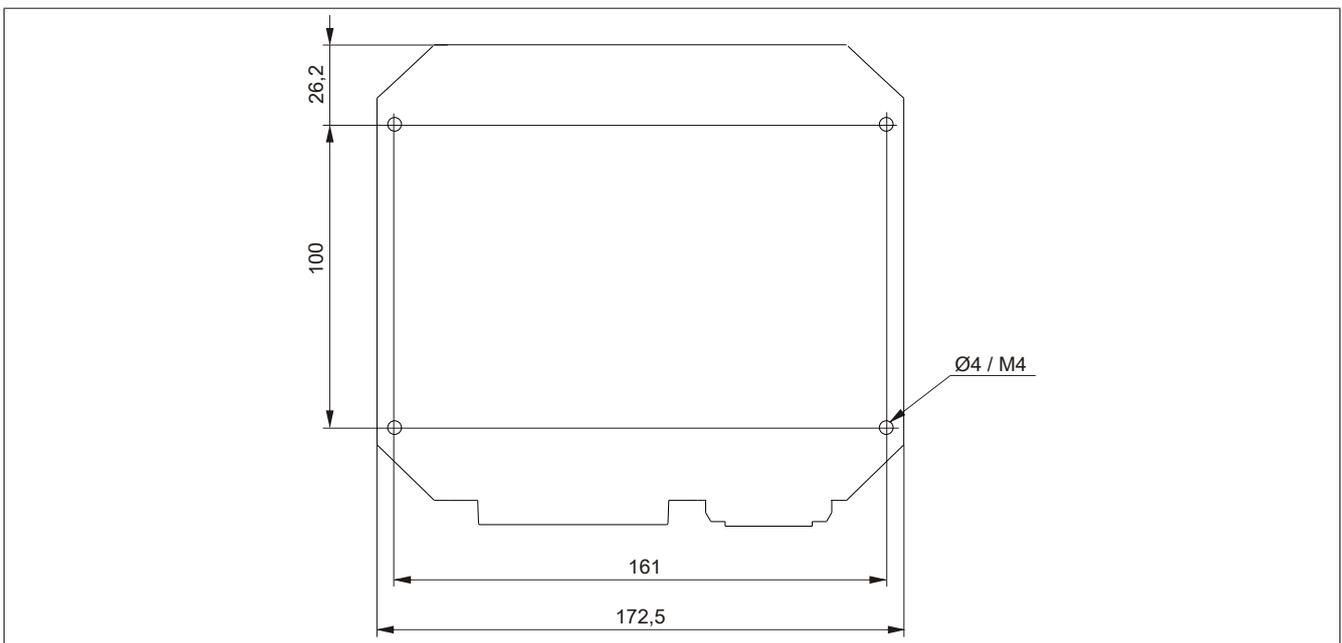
4MPCBX.0000-00 - Bohrschablone
